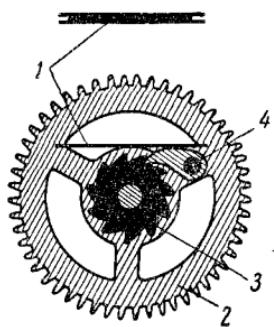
Изготовление пружины собачки заводного колеса хода будильника и настольных часов:
